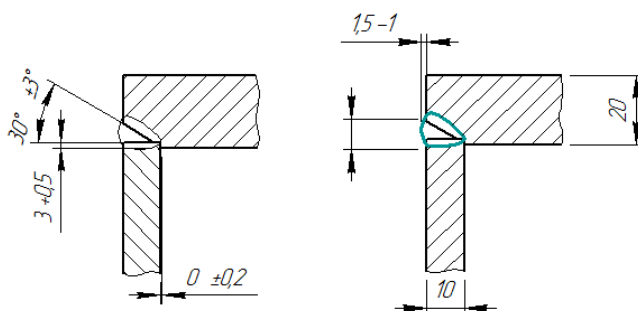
Форма и размеры сварного соединения I
